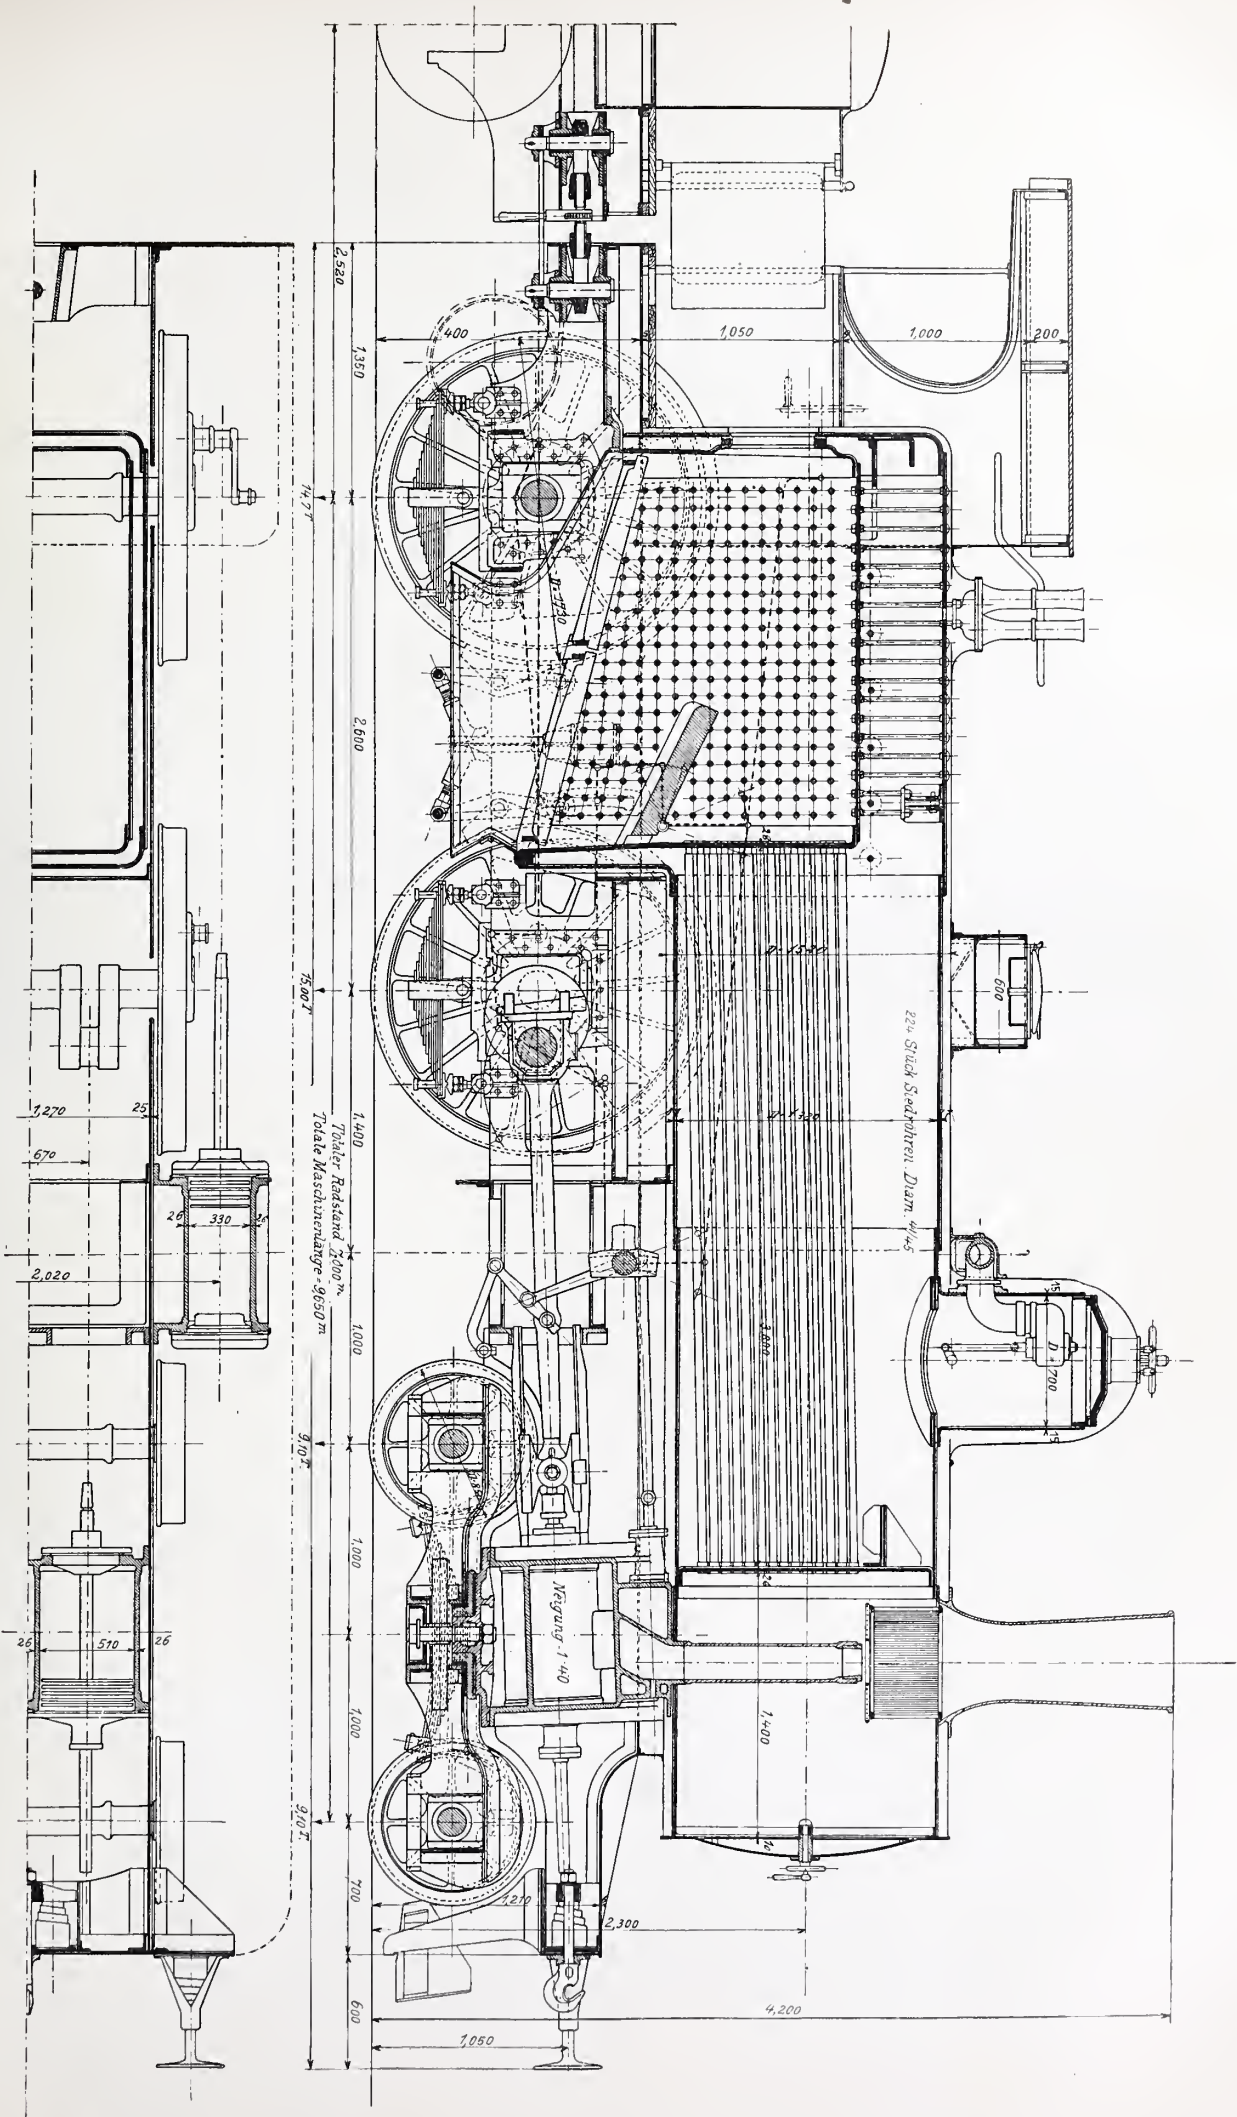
Längenschnitt der Maschine und Horizontalschnitt durch die Cylinder.
